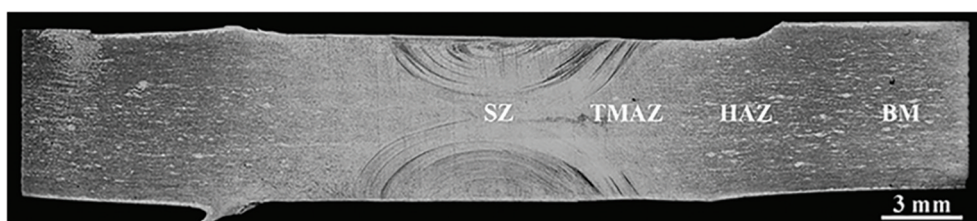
挤压态AZ31镁合金双面一体式(bobbin-tool)搅拌摩擦焊接头宏观形貌
